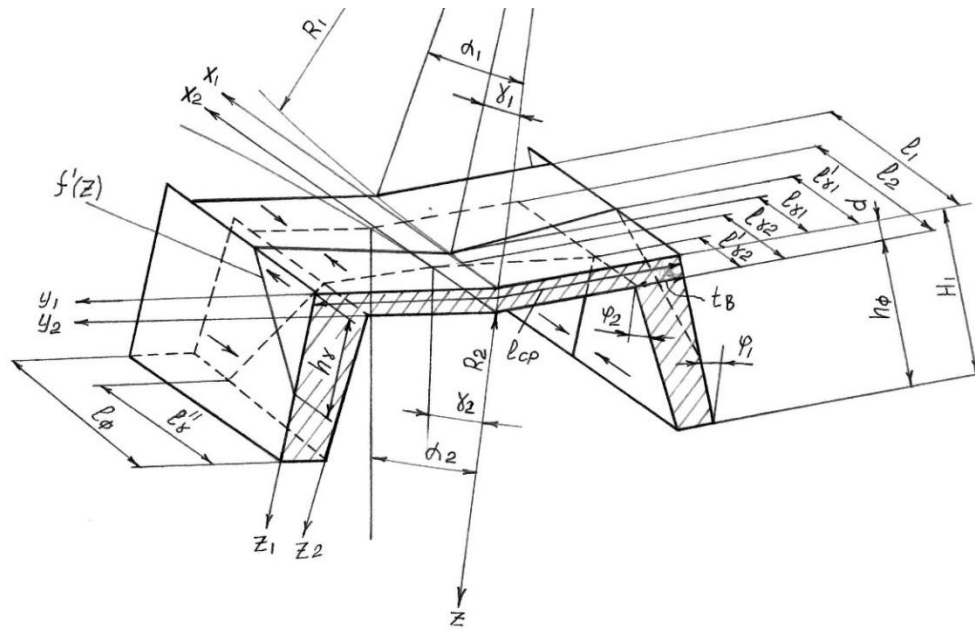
Принятая система координат и обозначения к определению нейтральной линии на контактной поверхности металла с валками в двухвалковом швеллерном калибре
